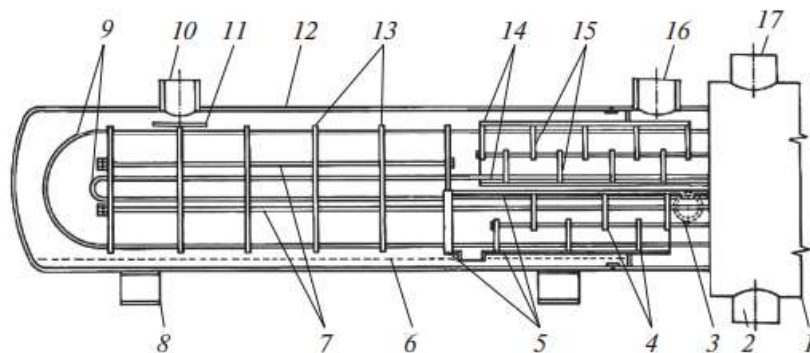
Конструкция горизонтального подогревателя высокого давления.[6]
